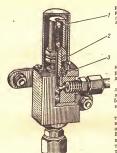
Регулировка регулятора давления: 1 — колпачок; 2 — контргайна; 3 — прокладка.
